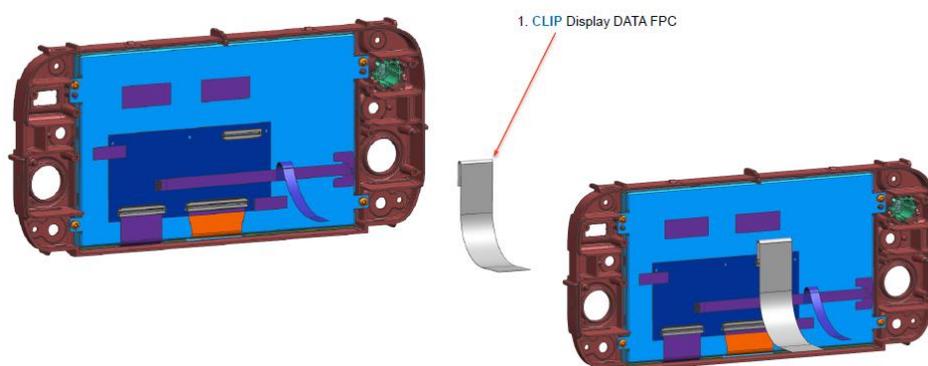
Front Panel – Exploded View – Assembly – Display DPC (Aptiv, 2019)
